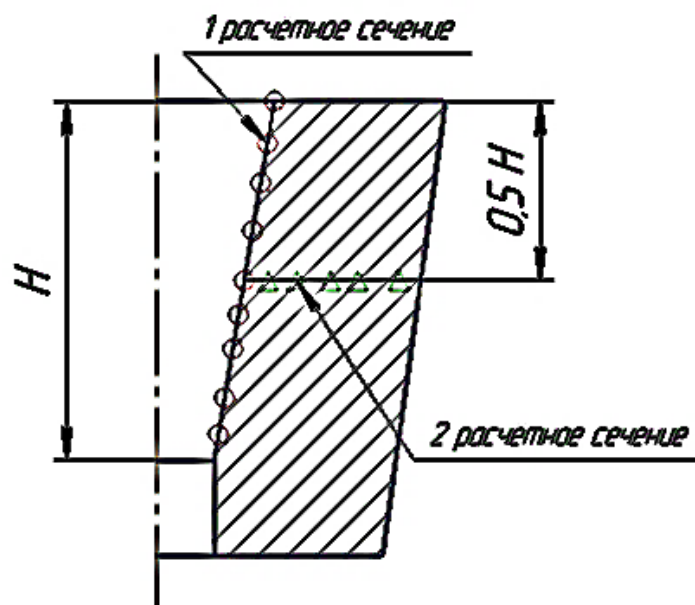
9 – Схема расчётных сечений исследуемой заготовки
